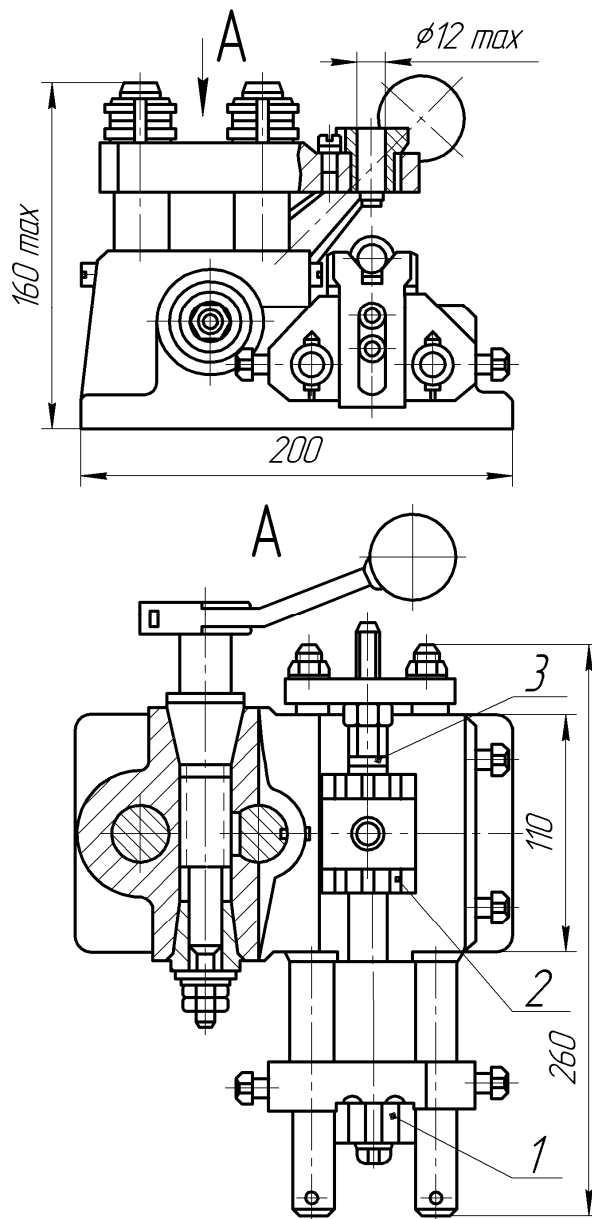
Будова й параметри кондуктора скальчастого з механічним затискачем для свердління отворів у циліндричних заготовках: 1, 2 – призми; 3 – упор
